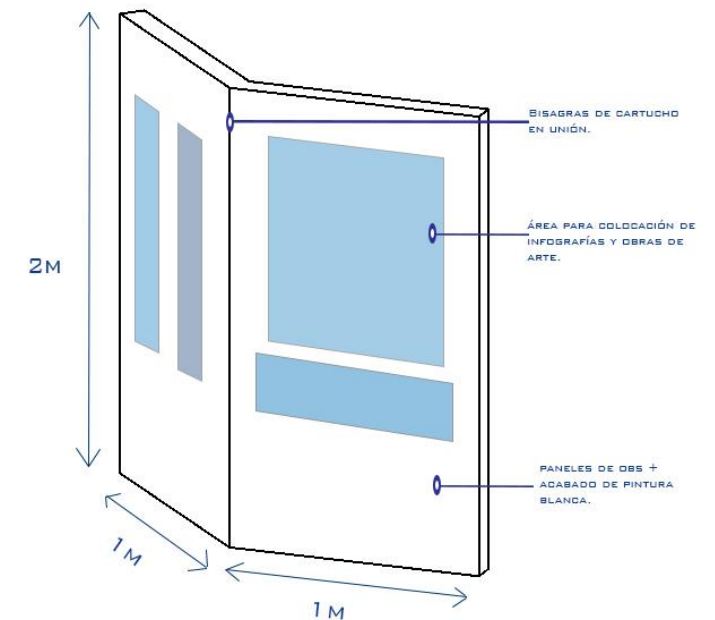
Detalle 3D panel de exposición. Fuente: Elaboración propia.
